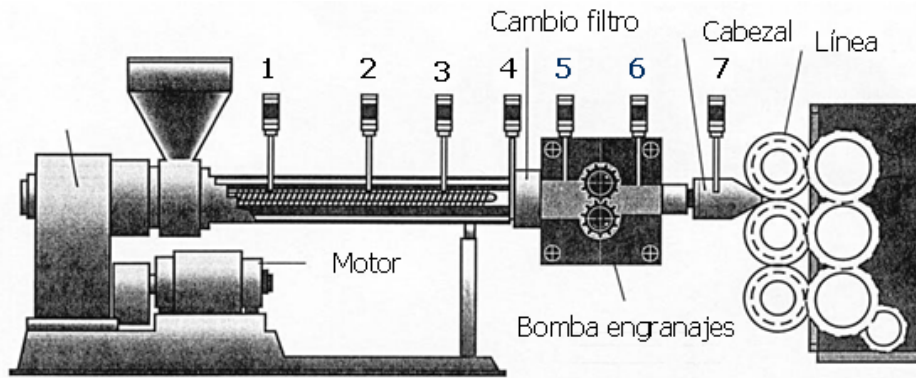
Esquema montaje de línea de extrusión con bomba de engranaje.
